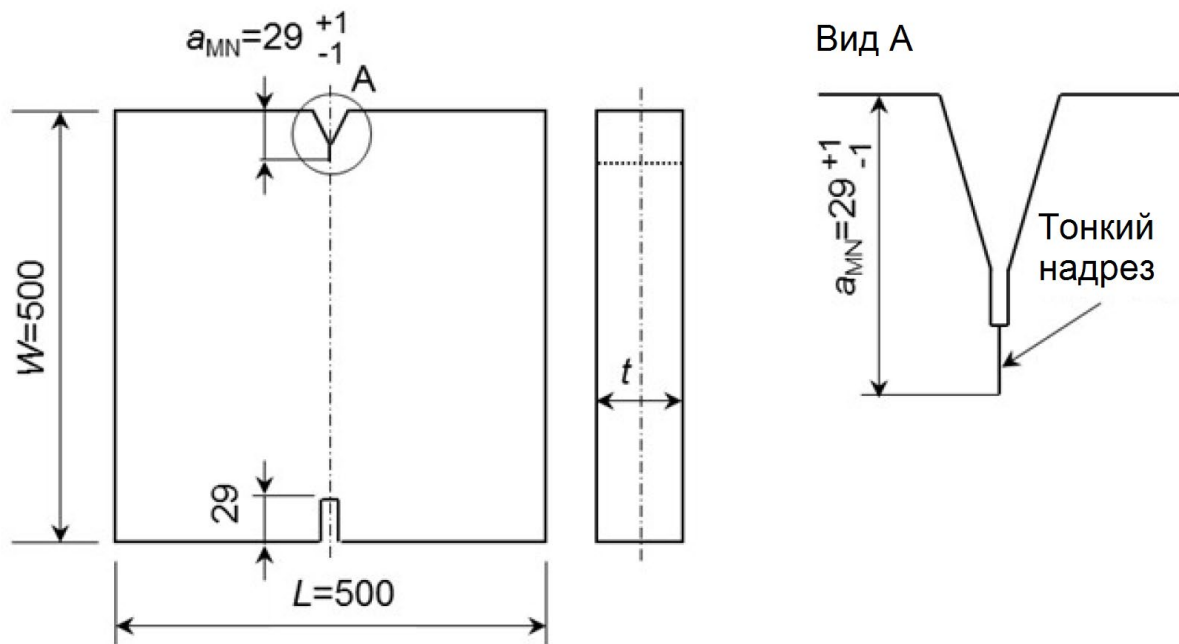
Размеры испытываемого образца для образования трещины ударной нагрузкой
